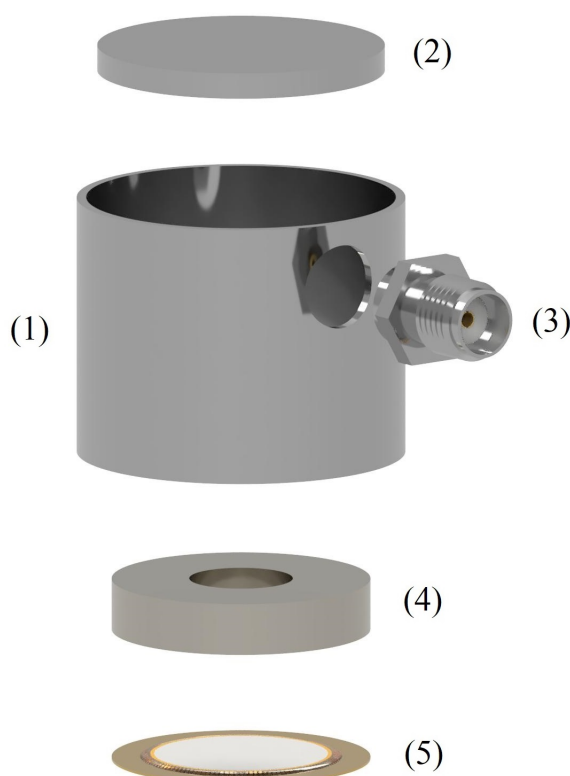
Perspectiva explodida do transdutor piezelétrico encapsulado. Fonte: Autor.
